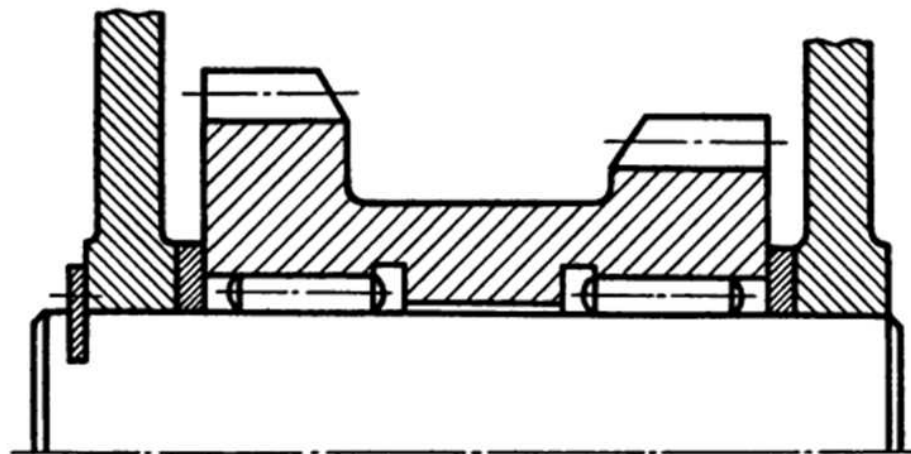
Блок зубчатых колес на подшипниках с игольчатыми роликами
